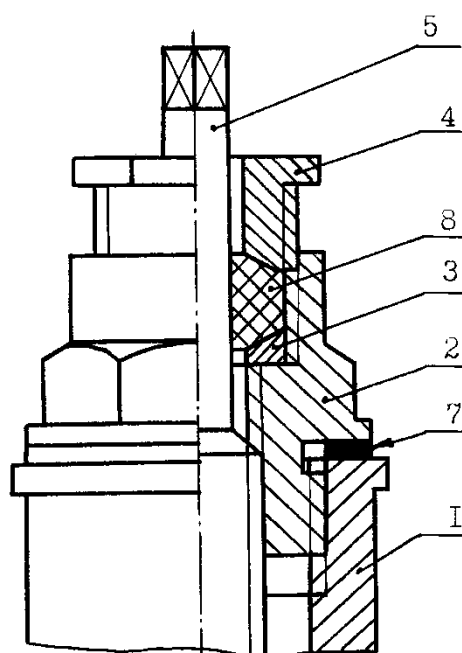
Конструкция сальникового устройства с втулкой резьбовой
